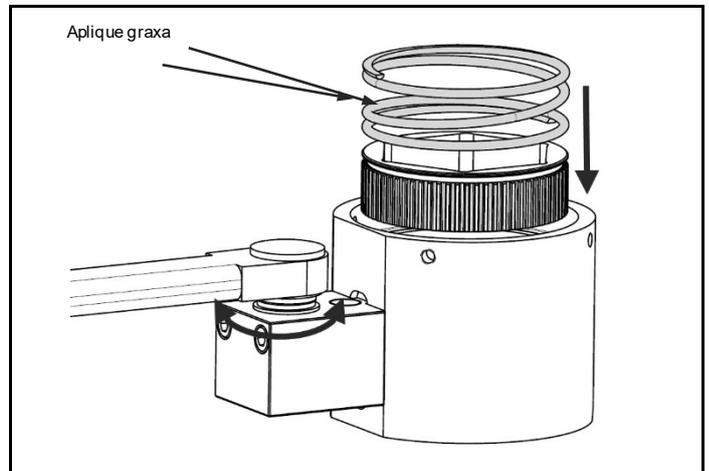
Aplique graxa, insira o soquete dentado, seguido por molas de compressão
